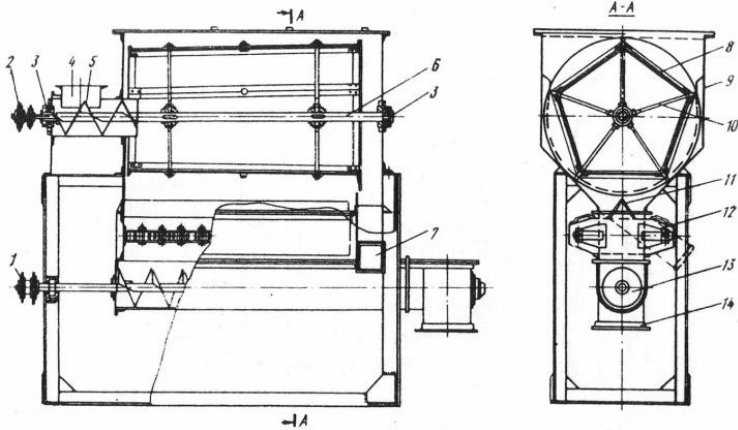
Пірамідальний бурат: 1, 2 – зірочки; 3 – підшипники; 4 – бункер; 5 – короткий шнек; 6 – вал; 7 – канал для домішок; 8 – барабан; 9 – корпус; 10 – спиці; 11 – щиток; 12 – магніти; 13 – відвідний шнек; 14 – вивантажувальний отвір
